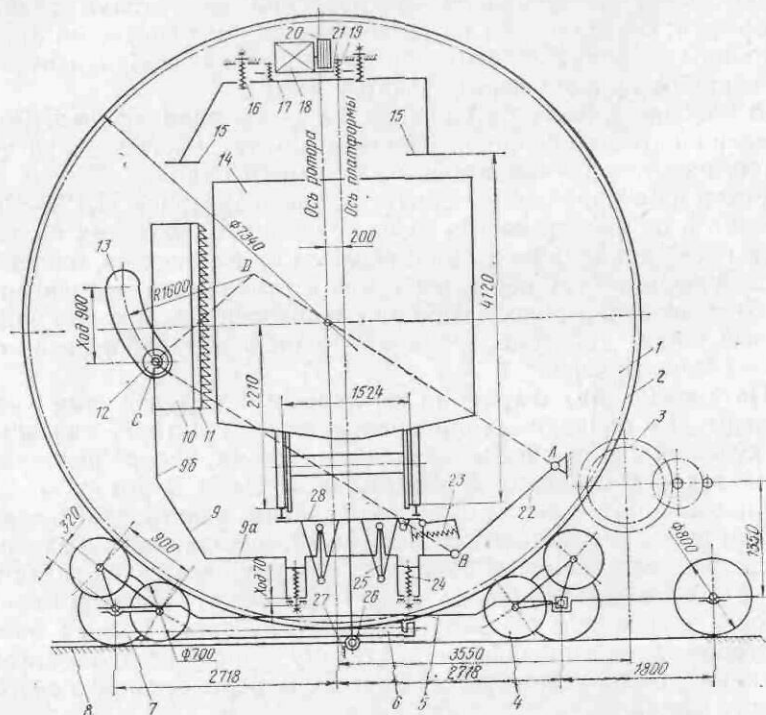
Схема ротора передвижного роторного вагонопрокидывателя с механизмами кантования ротора, зажима и очистки вагона
